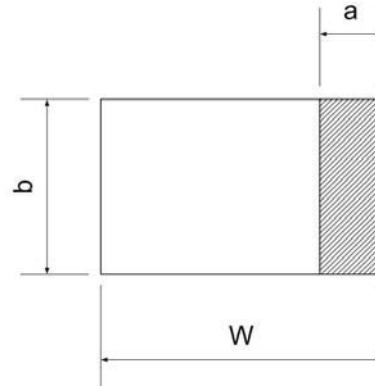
Querschnittsfläche eines rechteckigen Bauteils mit Oberflächenanriss
